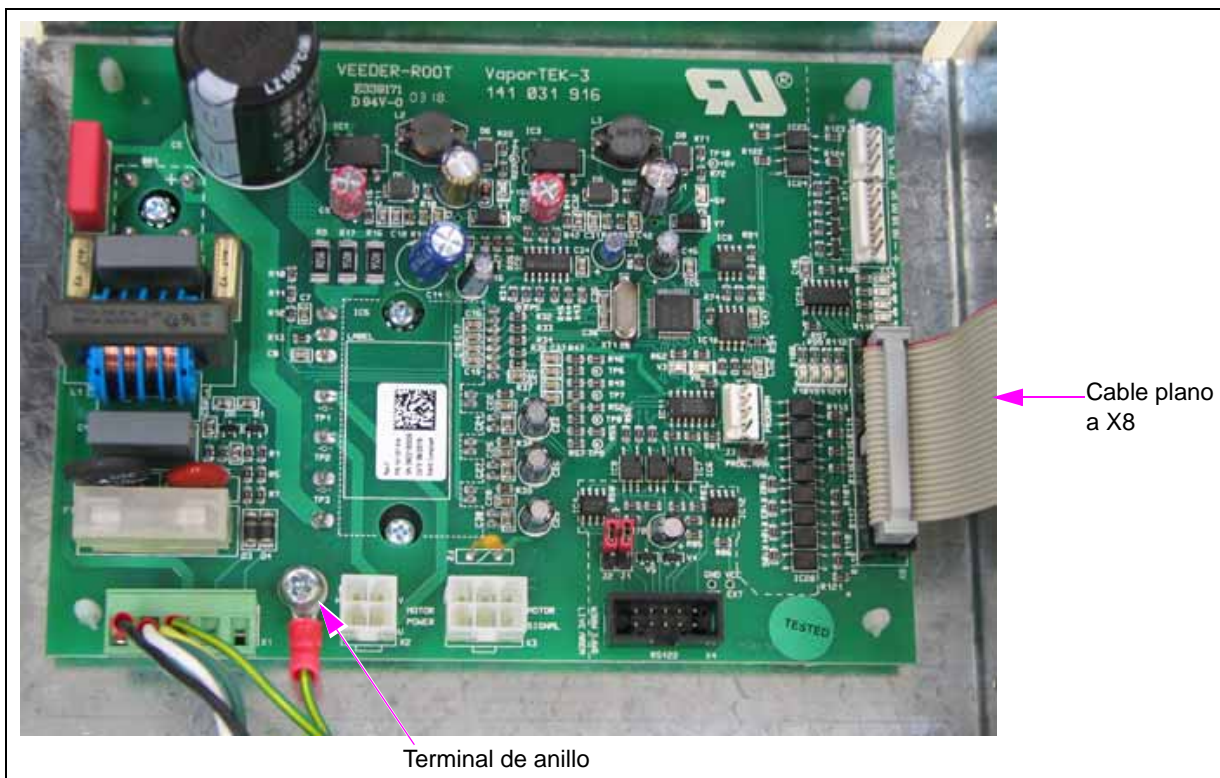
Conjunto de tarjeta del controlador de VaporTEK-3
